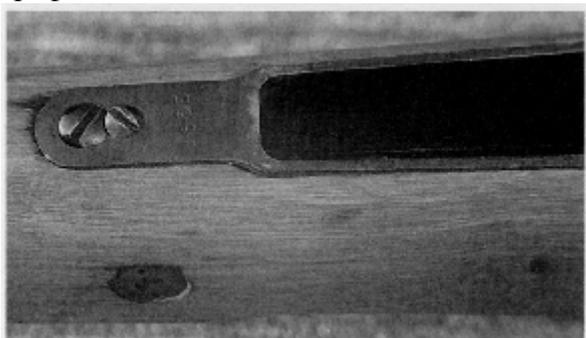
Помповая винтовка Ремингтон Модели 760, вид на приклад со снятым амортизатором отдачи. Существующее отверстие для стяжного болта (в которое вставляется стяжной болт для соединения ложи с ресивером) имеет правильный размер и форму для установки гасителя отдачи от C&H Research. Смотри раздел по Инерционному Приспособлению для Смягчения Отдачи дальше в этой главе. Если вы сверлите подобное отверстие по какой-либо
